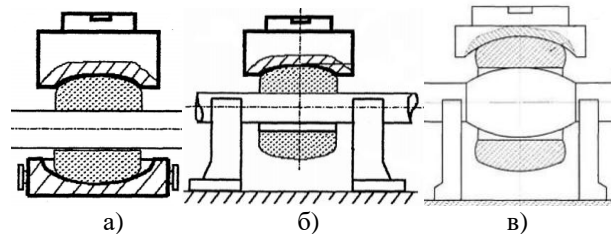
Способи отримання сферичних поковок: а – отримання сферичної заготовки; б – отримання поковки із зовнішньою сферичною поверхнею; в – отримання поковки із зовнішньою і внутрішньою сферичними поверхнями
